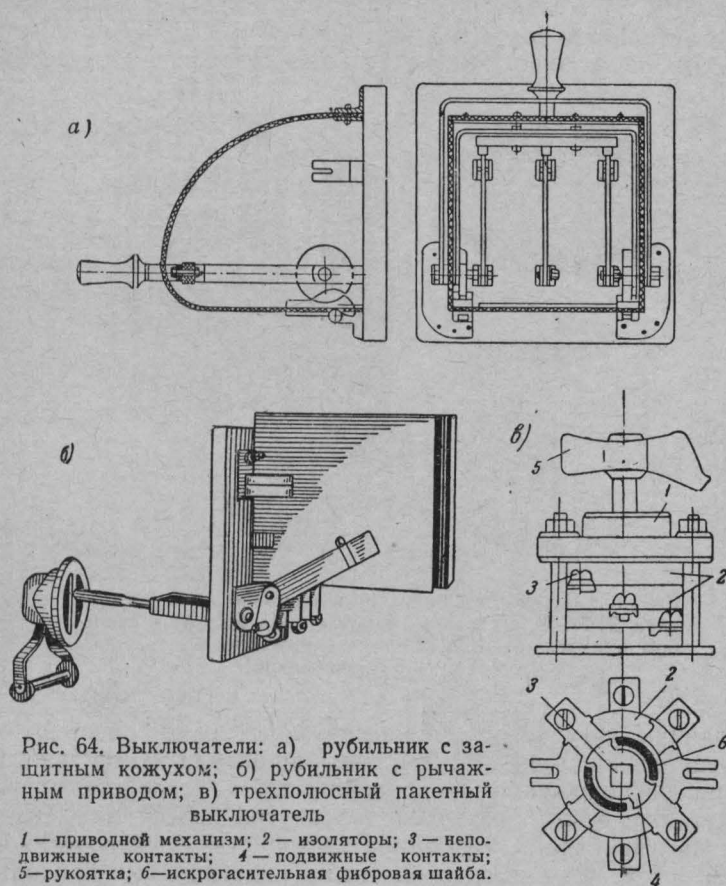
Выключатели: а) рубильник с защитным кожухом; б) рубильник с рычажным приводом; в) трехполюсный пакетный выключатель
